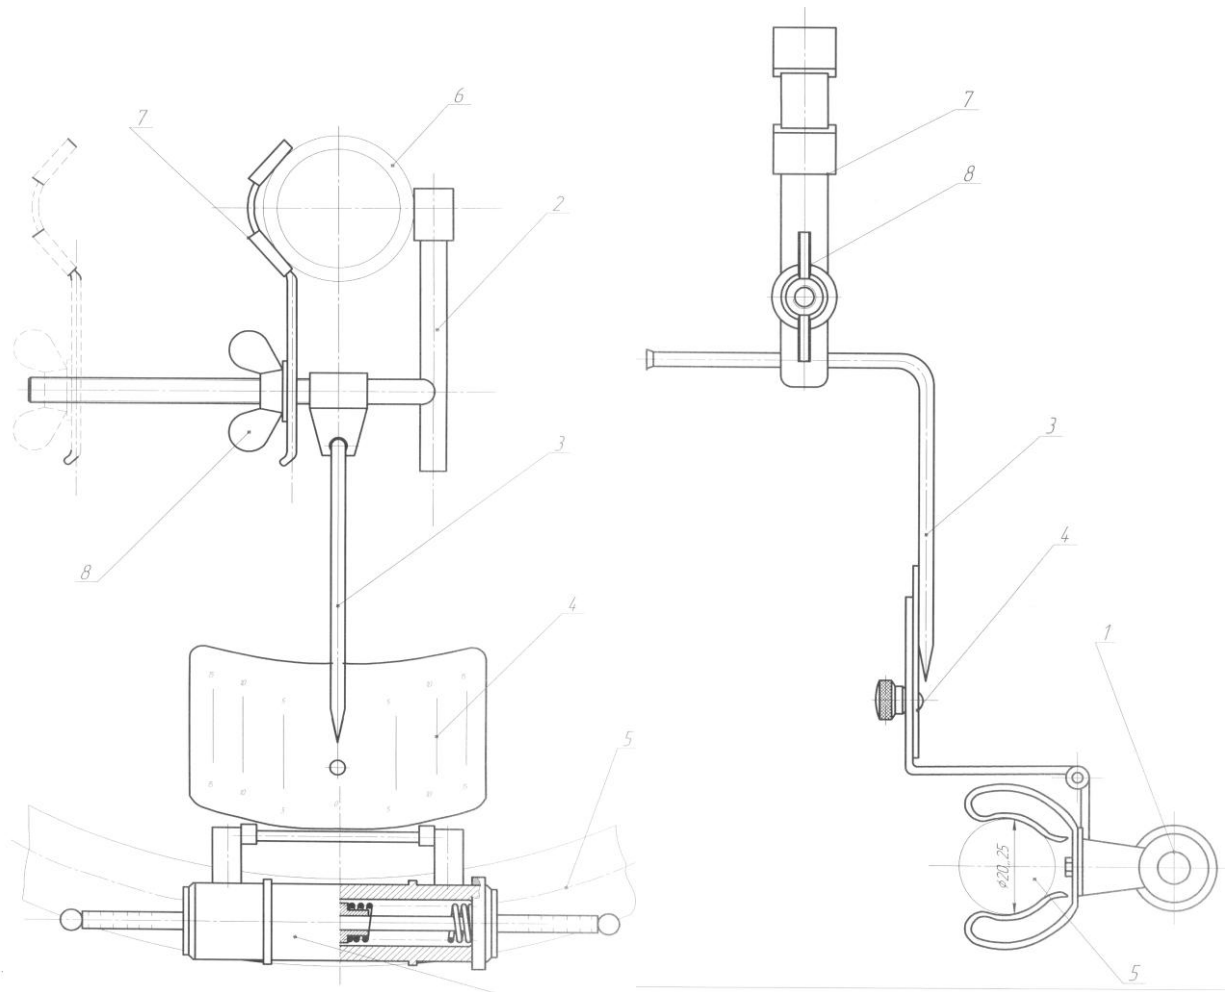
Устройство для замера люфта рулевого механизма
